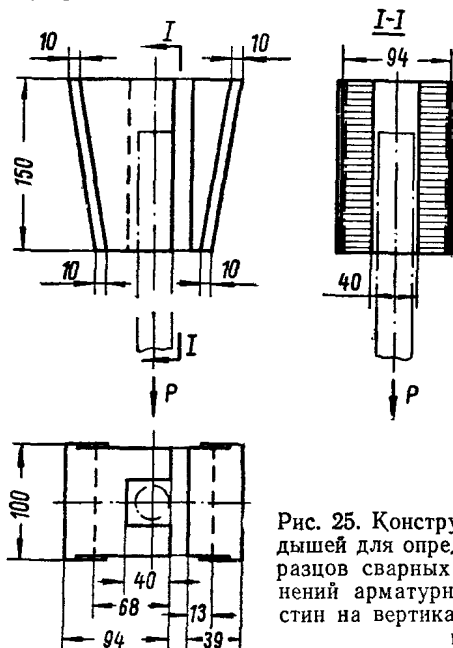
Конструкция клиновых вкладышей для определения прочности образцов сварных нахлесточных соединений арматурных стержней и пластин на вертикальных разрывных машинах
